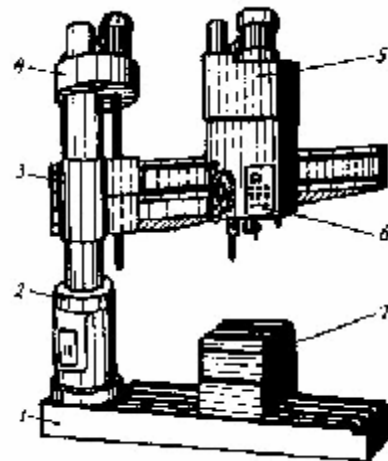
Общий вид радиально-сверлильного станка мод. 2M55
